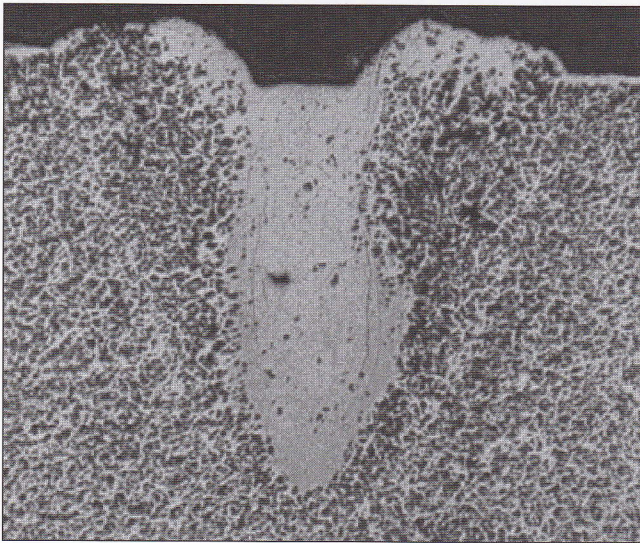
Macrografia del cordone di saldatura del composito A354-15%SiC
